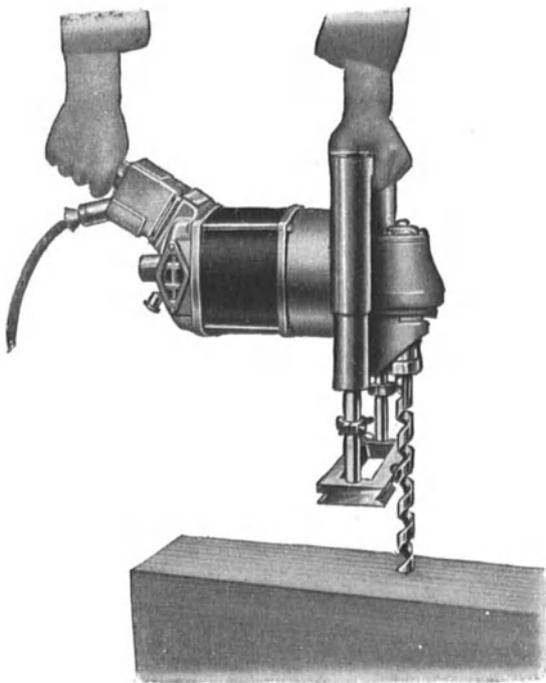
Handmaschine wie Abb. 71, zum Bohren eingerichtet. Die gleiche Maschine kann auch als Abläng-Kettensäge (ähnlich Abbildung 72) verwendet werden.
